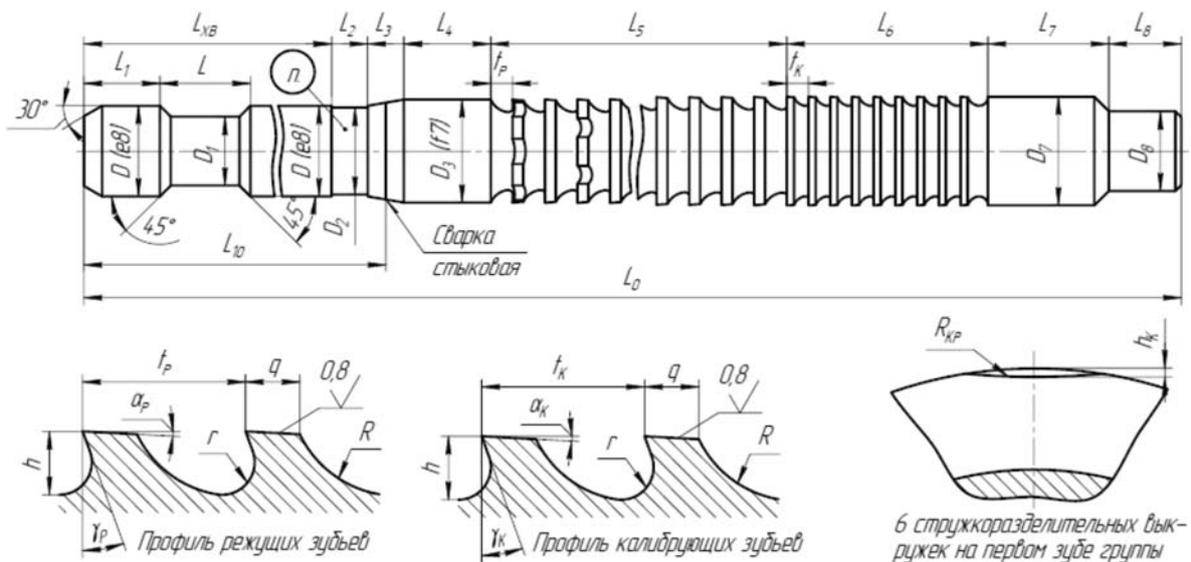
Протяжка для обработки цилиндрического отверстия
